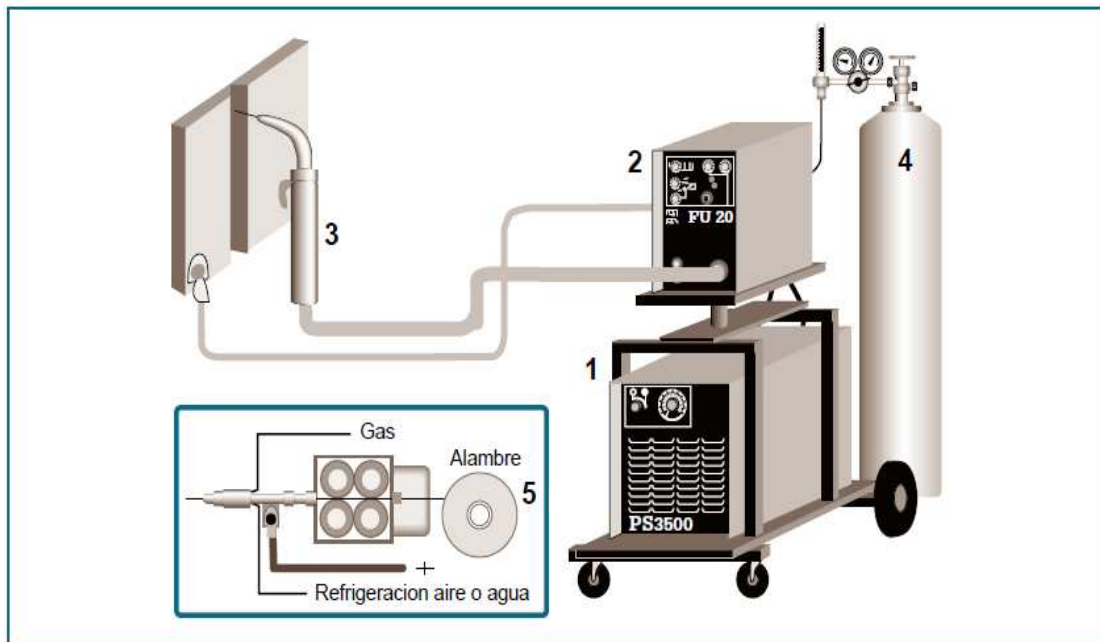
Proceso de Soldadura GMAW o MIG/MAG indicando sus partes.
